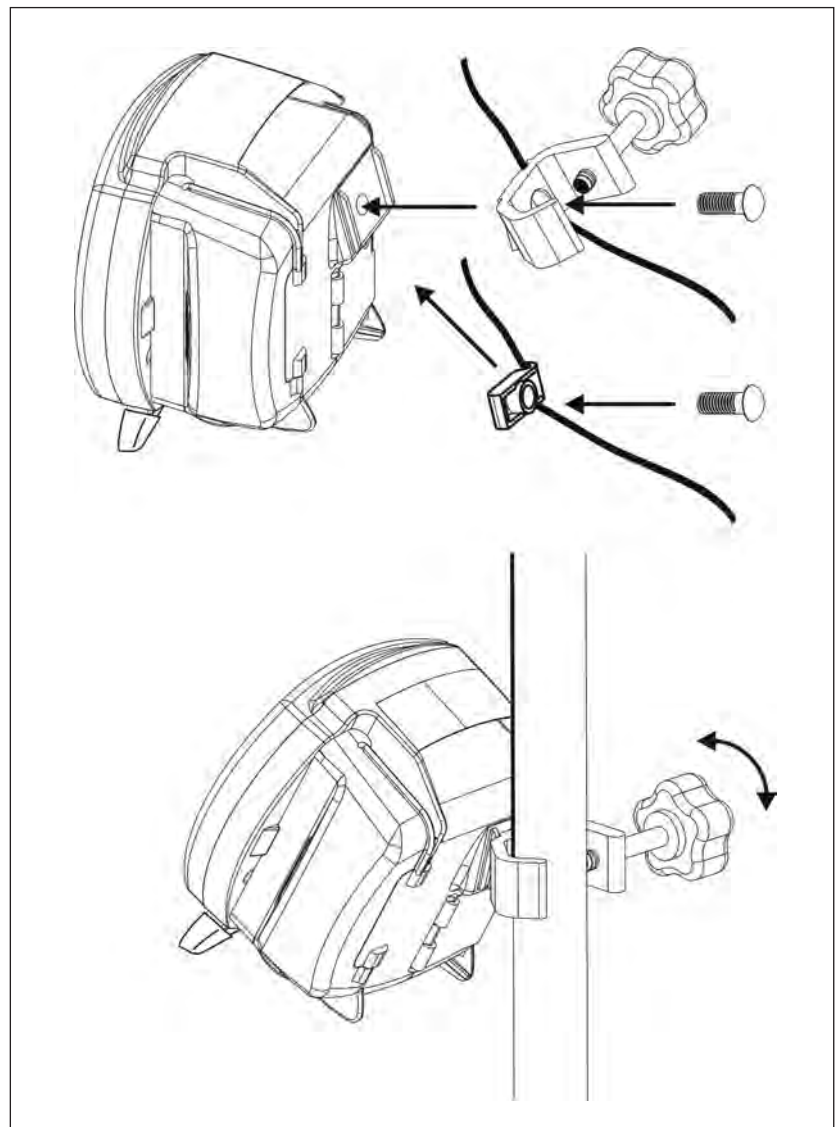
Ligar e utilizar o clampe para montagem em suporte ou o clipe do cabo.
